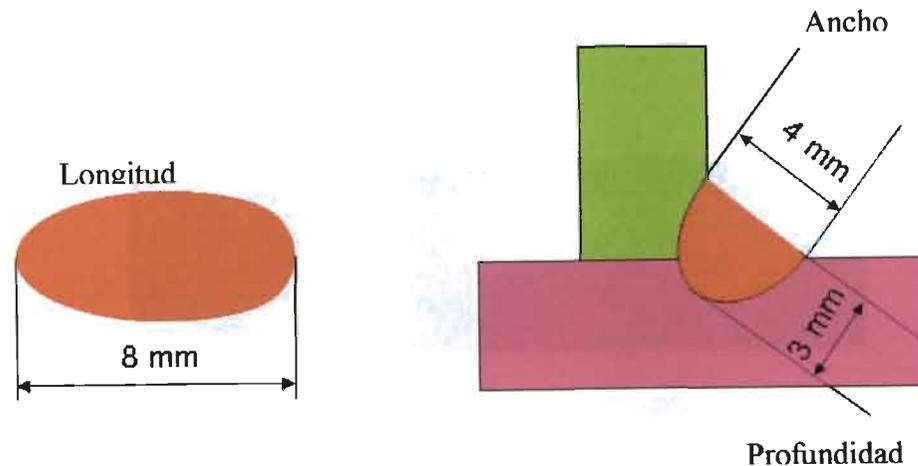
Información referente del charco de soldadura. [9]
